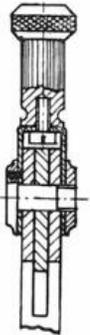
Kopf wie Fig. 2, aber mit Bügel:
